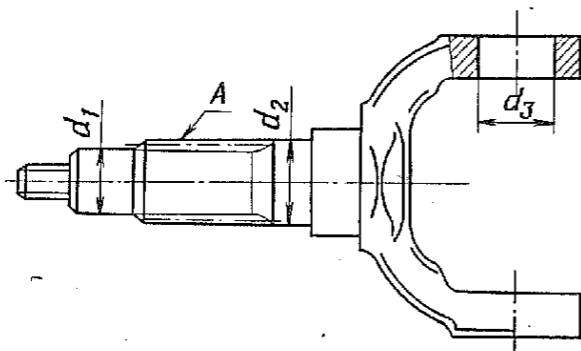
Вилка ведомая карданного шарнира полуоси (вал ведущей шестерни колесного редуктора)
